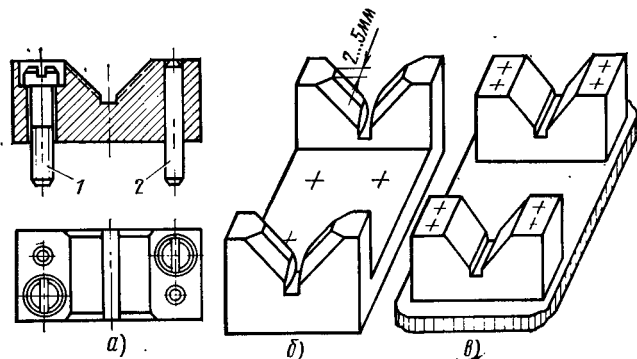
Опорные призмы для установки заготовок по внешним цилиндрическим поверхностям:
